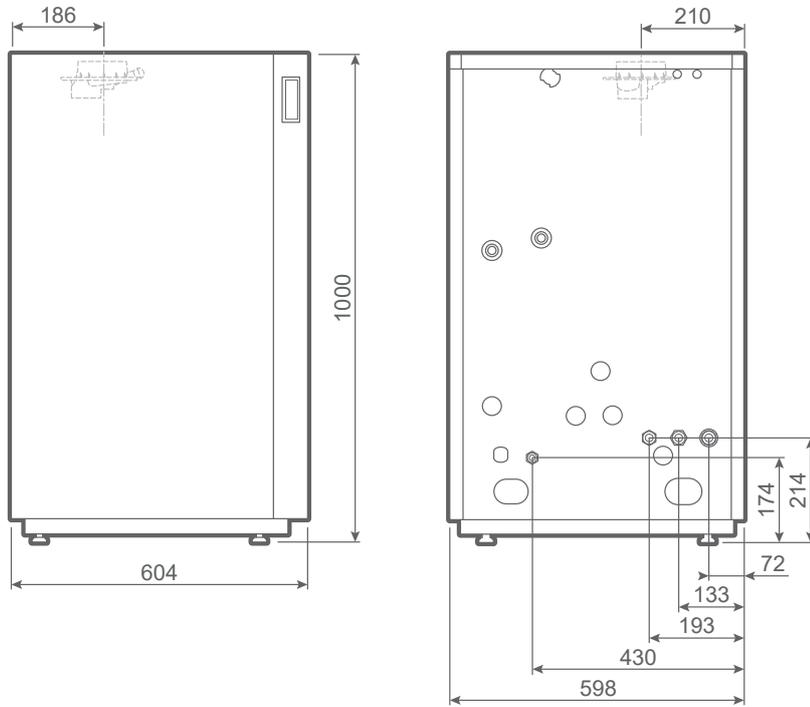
Dimensioni - Solo riscaldamento (in mm)
